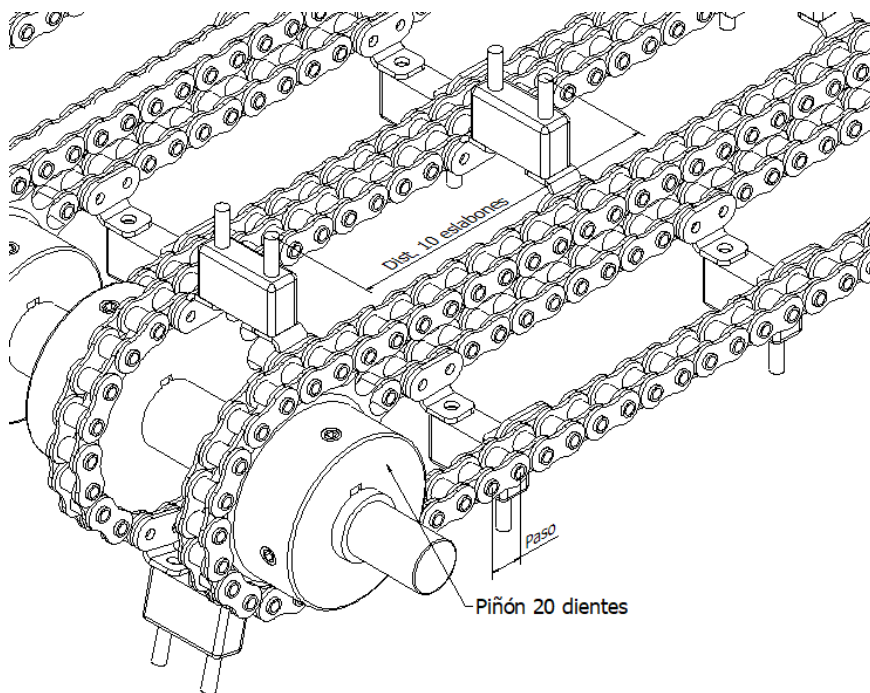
DETALLE SEPARACIÓN ENTRE ÍNDICES Y ELEMENTOS DE CADENA
